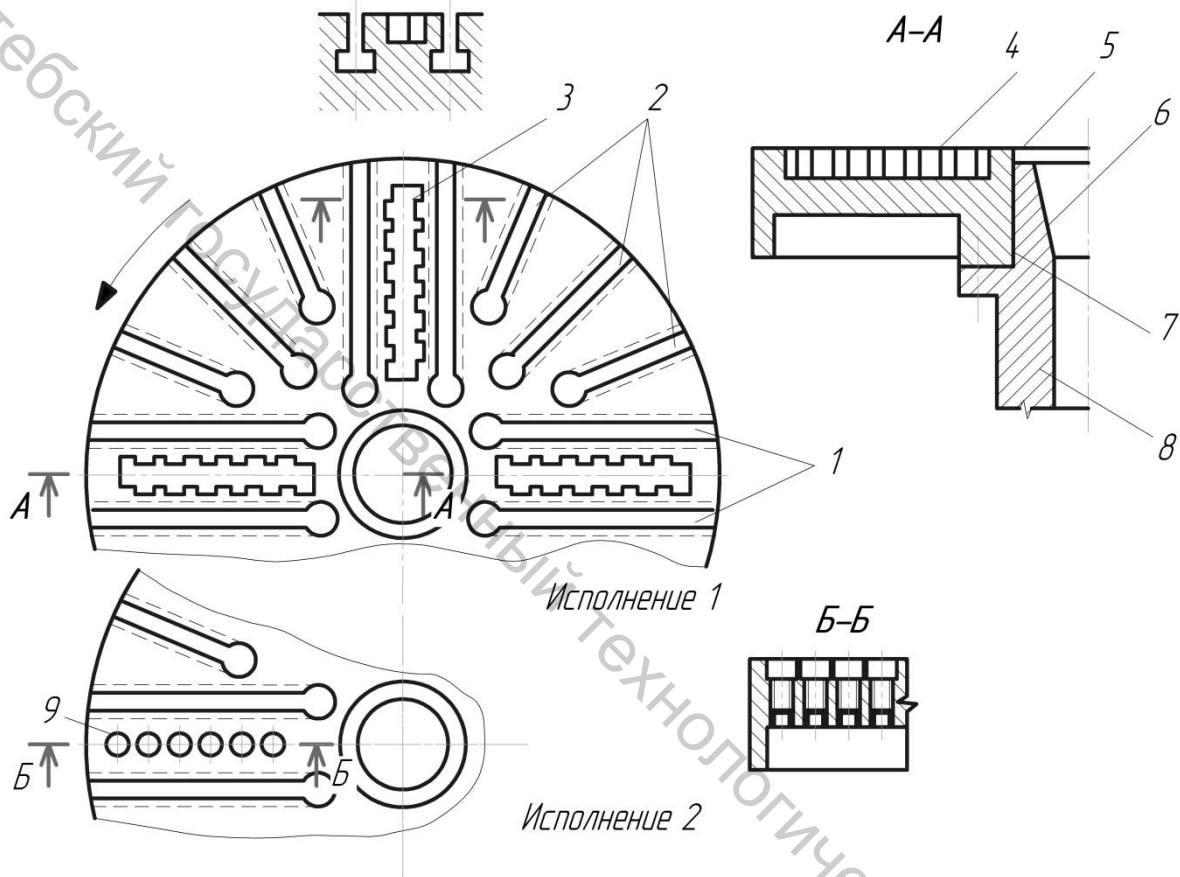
Планшайба(7) шпинделя(8) токарного карусельного станка:
